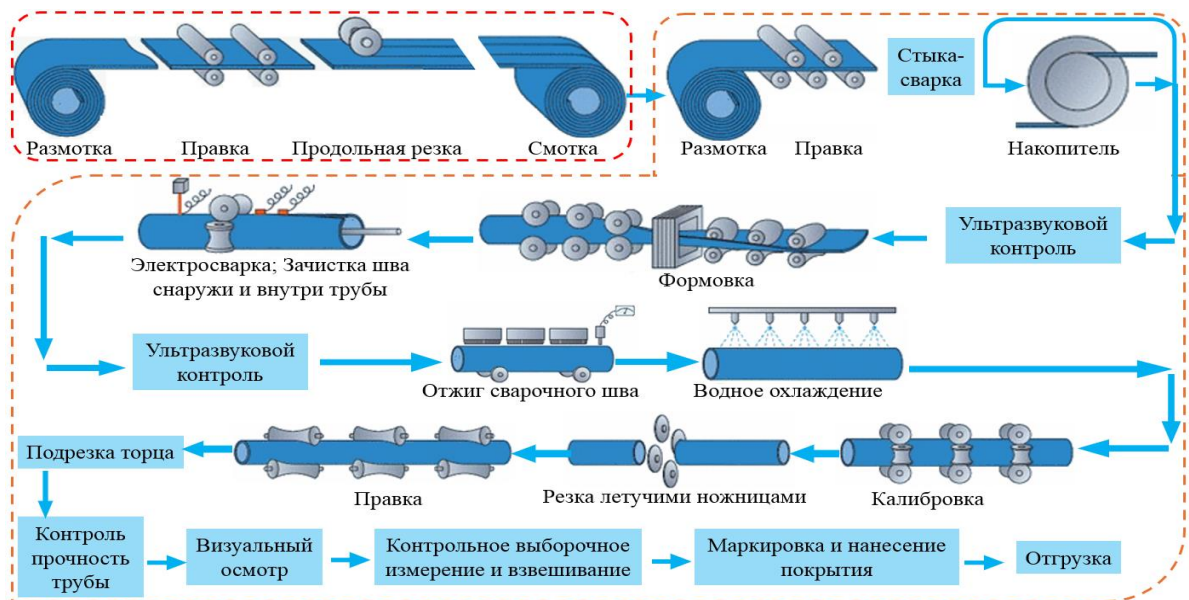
Общая схема производства сварных труб
